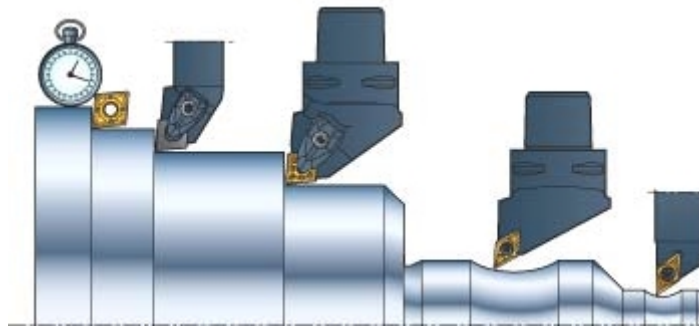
Exemplo do Processo de Usinagem-Tornear [70].
